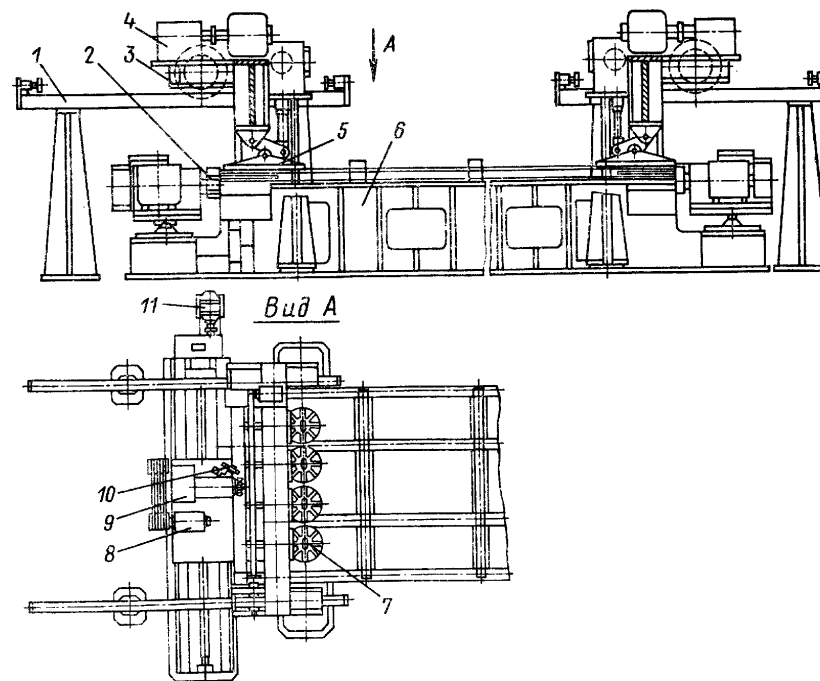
Станок для кислородной обрезки и фрезерования кромок пакета листов:
